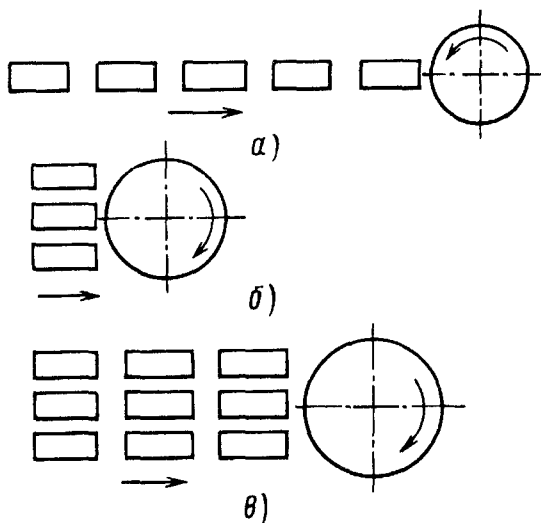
Схемы возможной установки деталей для обработки
